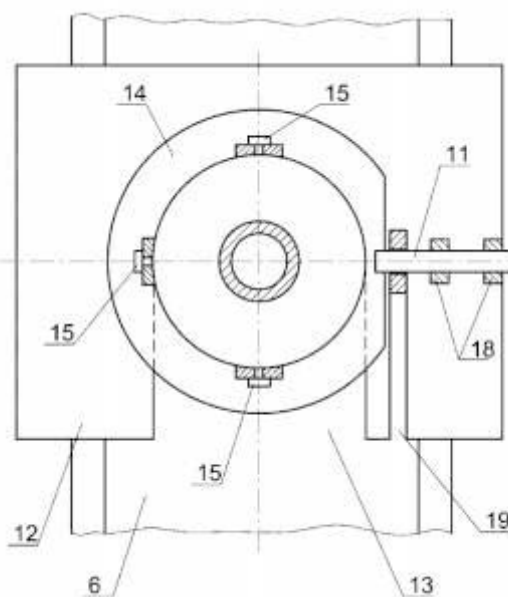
Вид сверху мобильного устройства для отбора пробы жидкого металла из металлотракта
